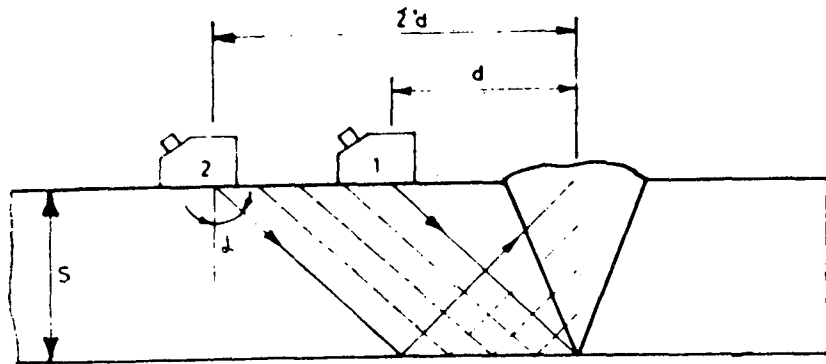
Desplazamiento transversal del palpador respecto del eje del cordón de soldadura, en el ensayo por ultrasonido.
